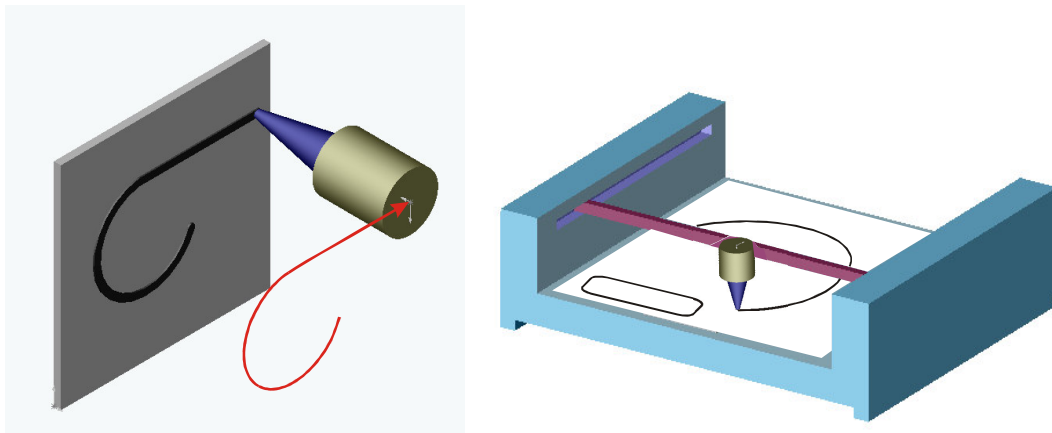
Esquema de uma impressão vetor, realizando o desenho mediante um movimento contínuo do cabeçote de impressão.
